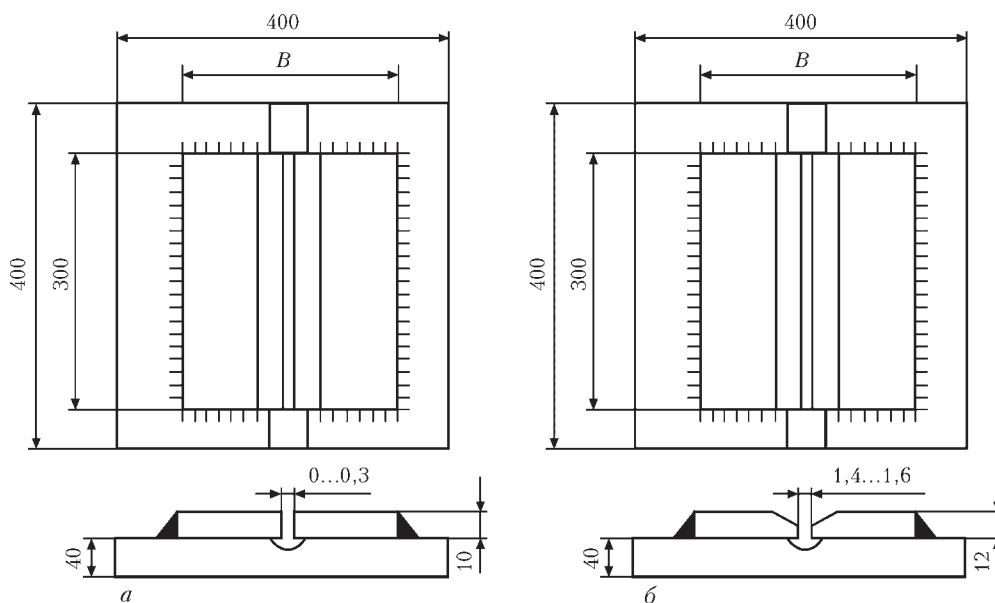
Технологическая проба с регулируемой жесткостью для гибридной и лазерной (а) и дуговой сварки (б)
